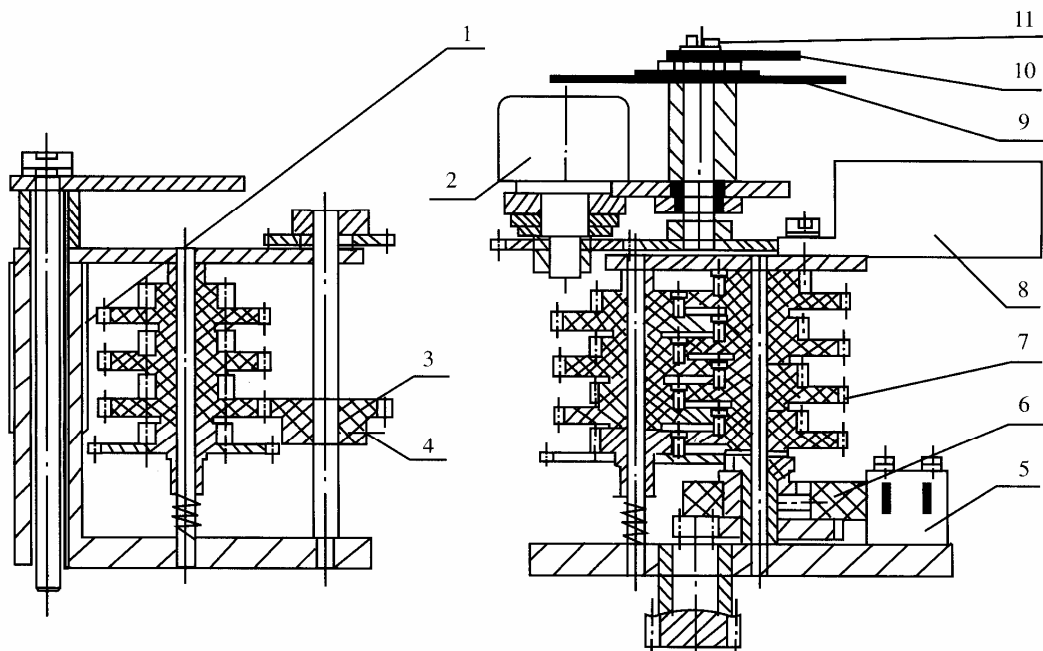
可调转圈数开度机构 Fig.9 adjustable valve position indicating mechanism
